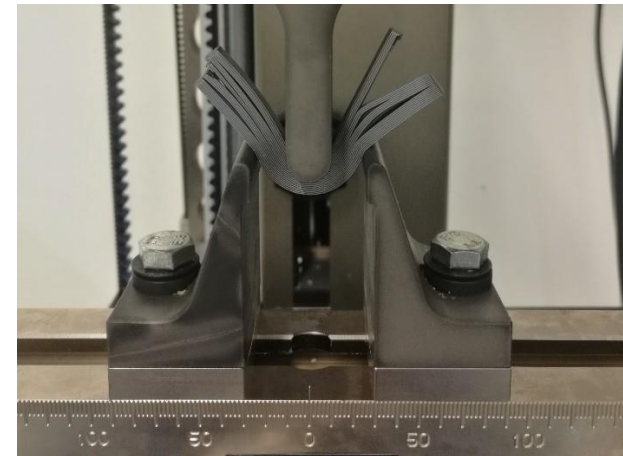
Rupture de la poutre en PLA lors d'un essai de flexion 3 points
